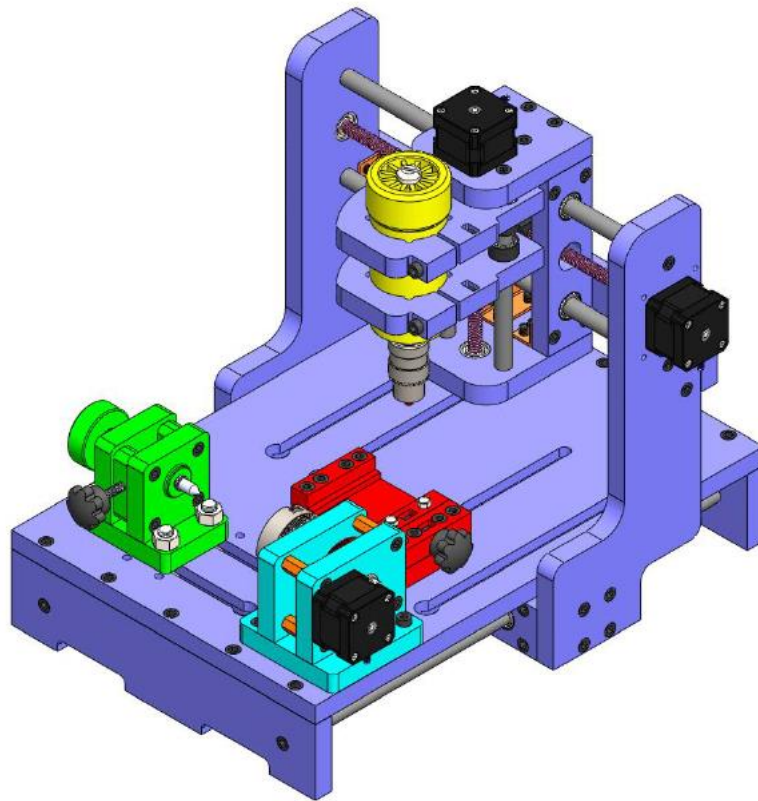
Просторова модель вертикально-фрезерного верстата
